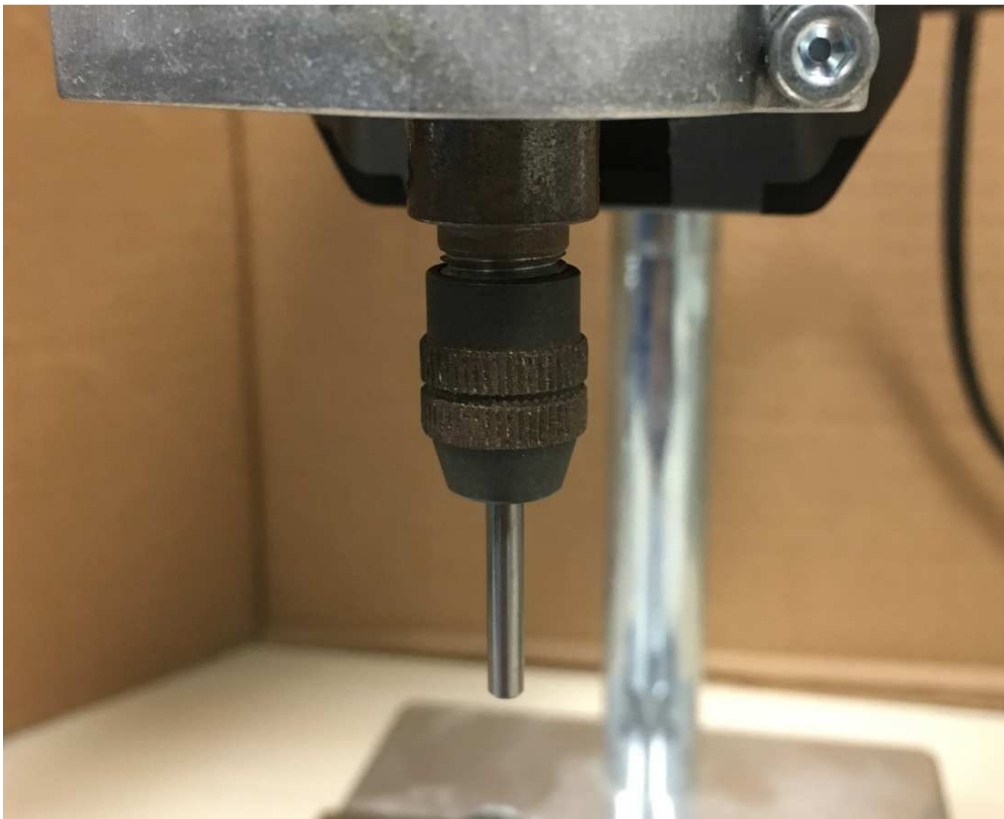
Imagen detalle de la pieza cilíndrica instalada en el mandril del taladro.
